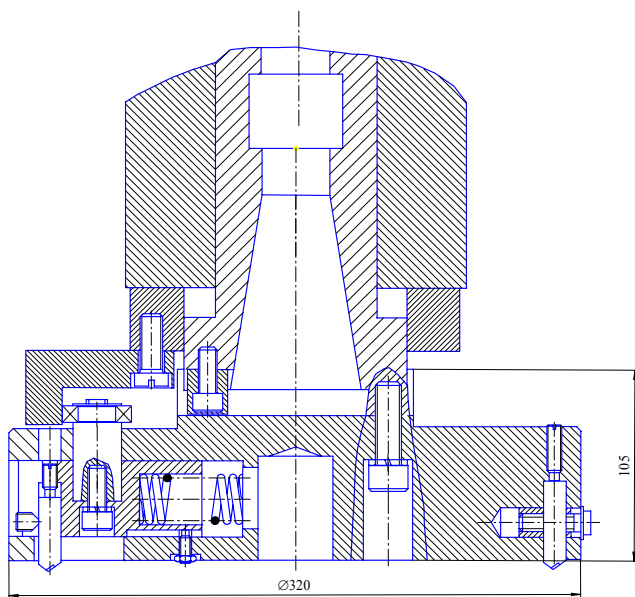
Установка фрезы с комбинированной схемой резания на станке
